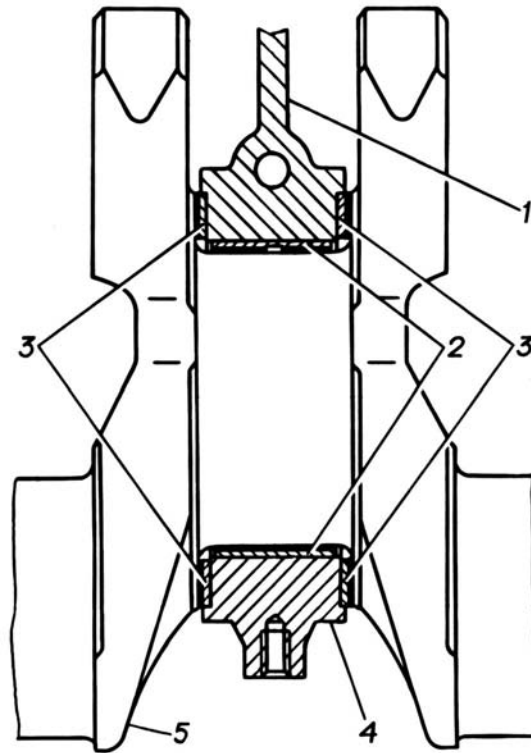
Средний (упорный) подшипник коленчатого вала: 1 - блок цилиндров; 2 - вкладыши подшипника; 3 - упорные полушайбы; 4 - крышка подшипника; 5 - коленчатый вал
